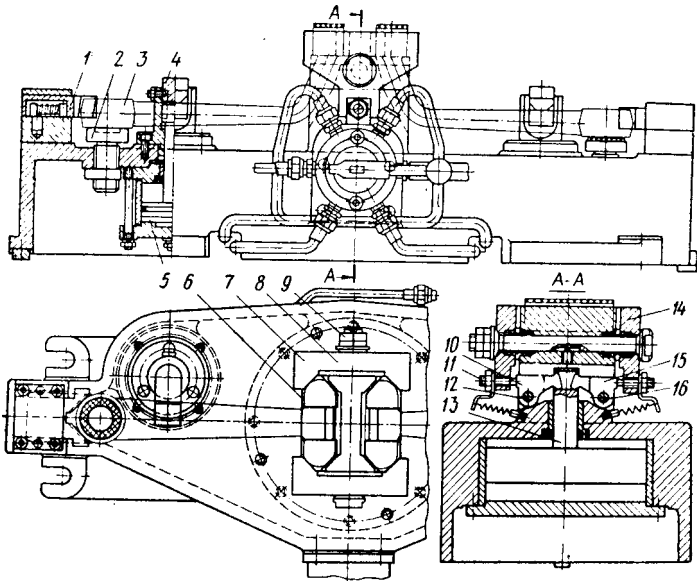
Двухместное приспособление для фрезерования изогнутых рычагов
